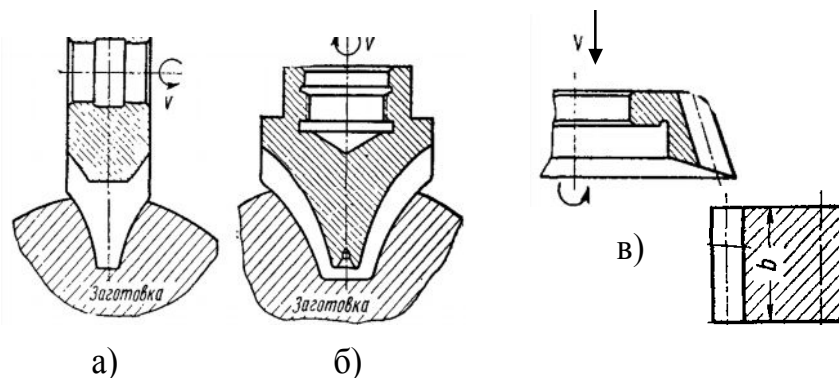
Нарезание зубчатых колес методом копирования: а – обработка дисковой модульной фрезой; б – обработка пальцевой модульной фрезой; в – обработка зуборезным долбяком.
